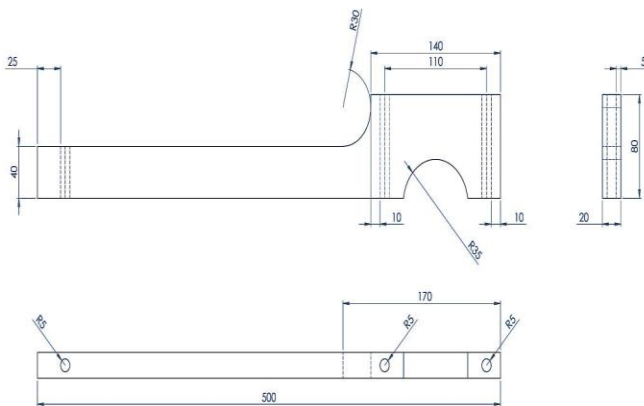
Dimensiones del brazo Principal placa superior. Fuente propia.
